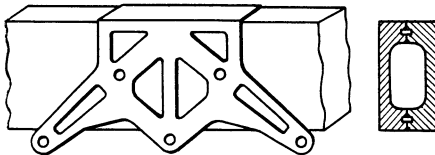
Umfassender Beschlag zur Verbindung eines Holzholmes mit Fachwerksgliedern.
